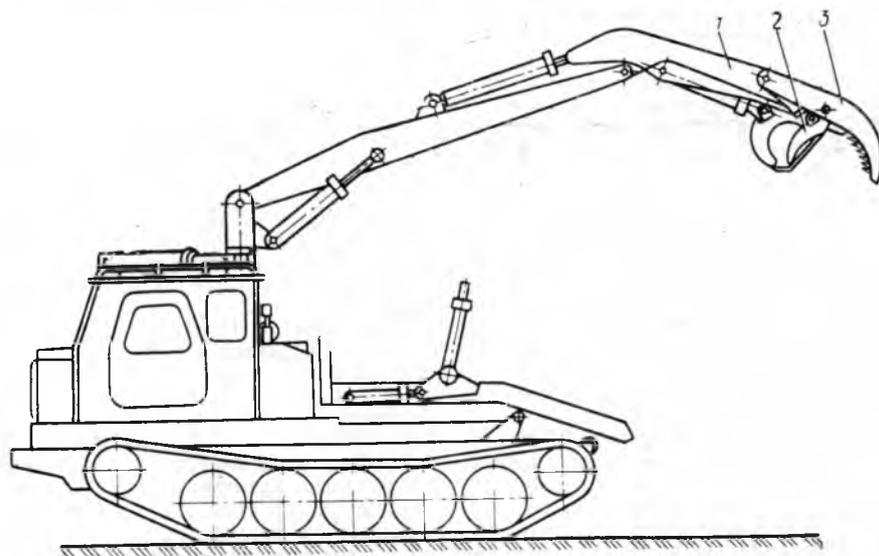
Механизм обрезки вершин на базе трактора ЛП-18А:
